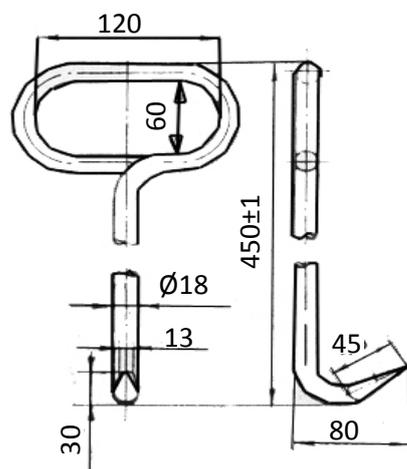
Крюк для открывания крышек колодцев пожарных гидрантов
